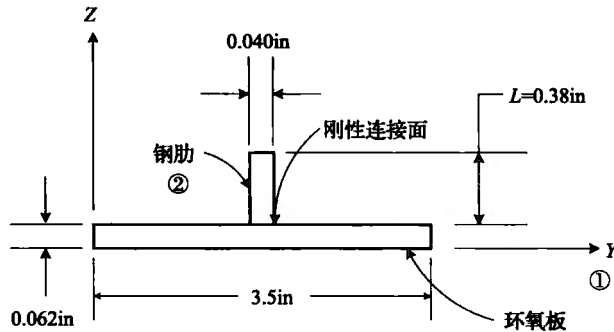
焊接到电路板上的加强肋截面尺寸
